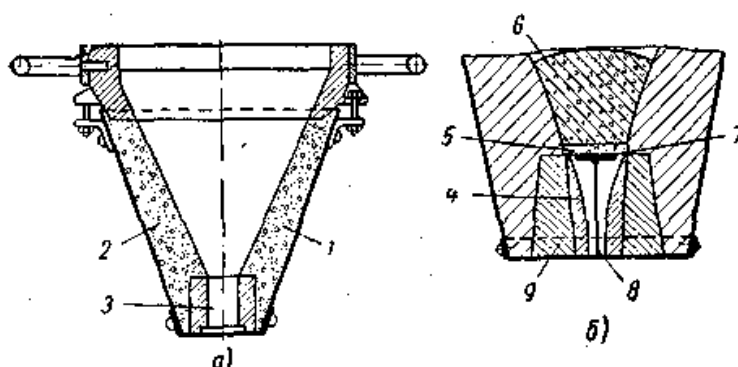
Тигель для сжигания термита а - тигель; б - область дна тигля; 1 - корпус; 2 - футеровка; 3 - стакан; 4 - шпатель-штука для выпуска расплава; 5 - магнезитовый песок; 6 - термит; 7 - асбестовый кружок; 8 - запорный гвоздь; 9 - стакан
